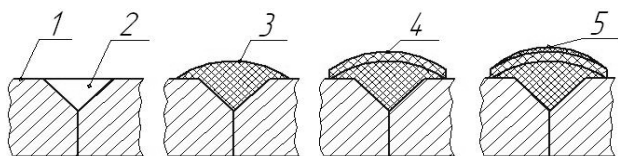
Схемы заделки трещины в корпусной детали композиционными полимерными материалами: 1 – деталь; 2 – трещина; 3 – слой клеевой композиции; 4 – слой стеклоткани; 5 – верхний слой клеевой композиции
